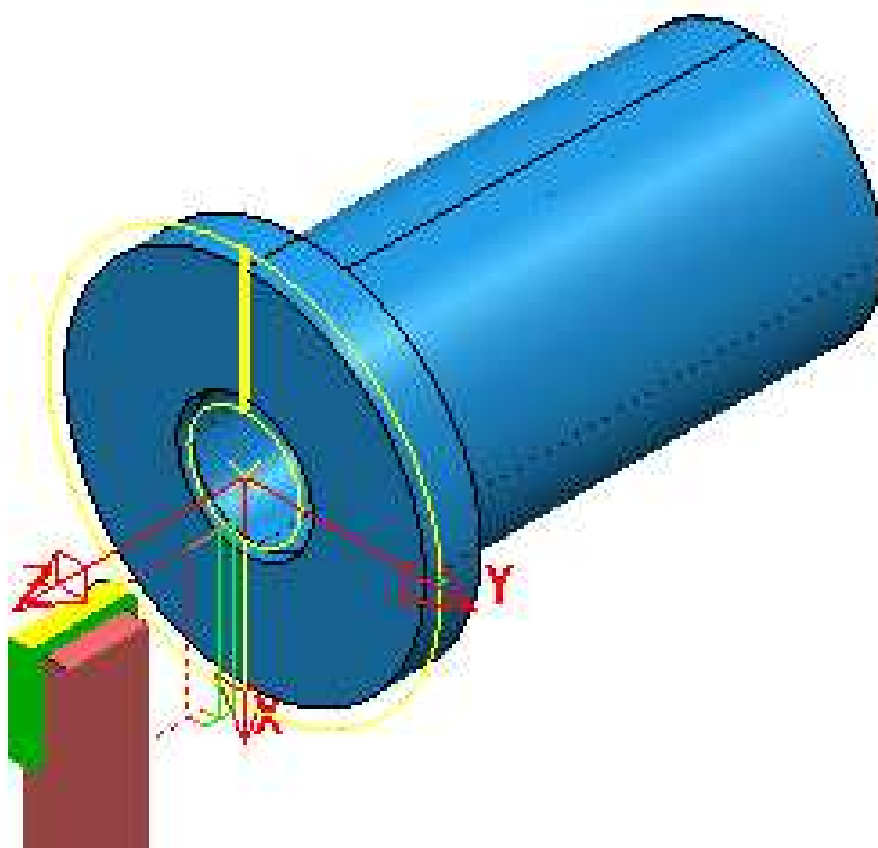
020 токарно-винторезная (подрезка торца)
